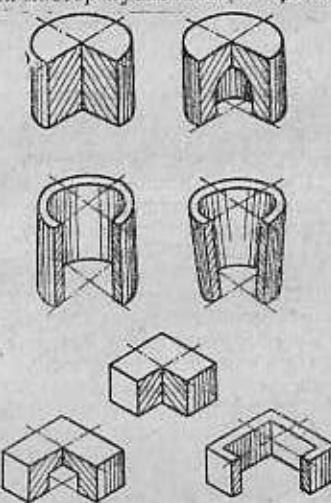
Заготовки для выдавливания мастер-пуансоном.
